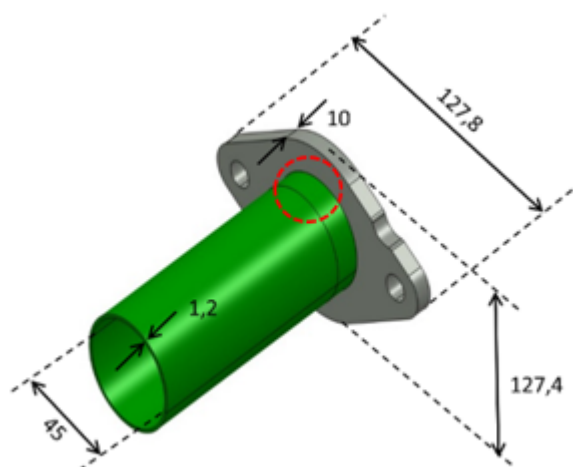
Desenho esquemático (dimensões em mm) do Conjunto de testes empregado neste estudo.
